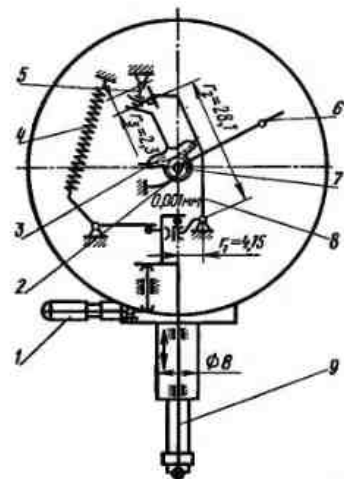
Рычажно-зубчатая измерительная головка типа 1МКМ
